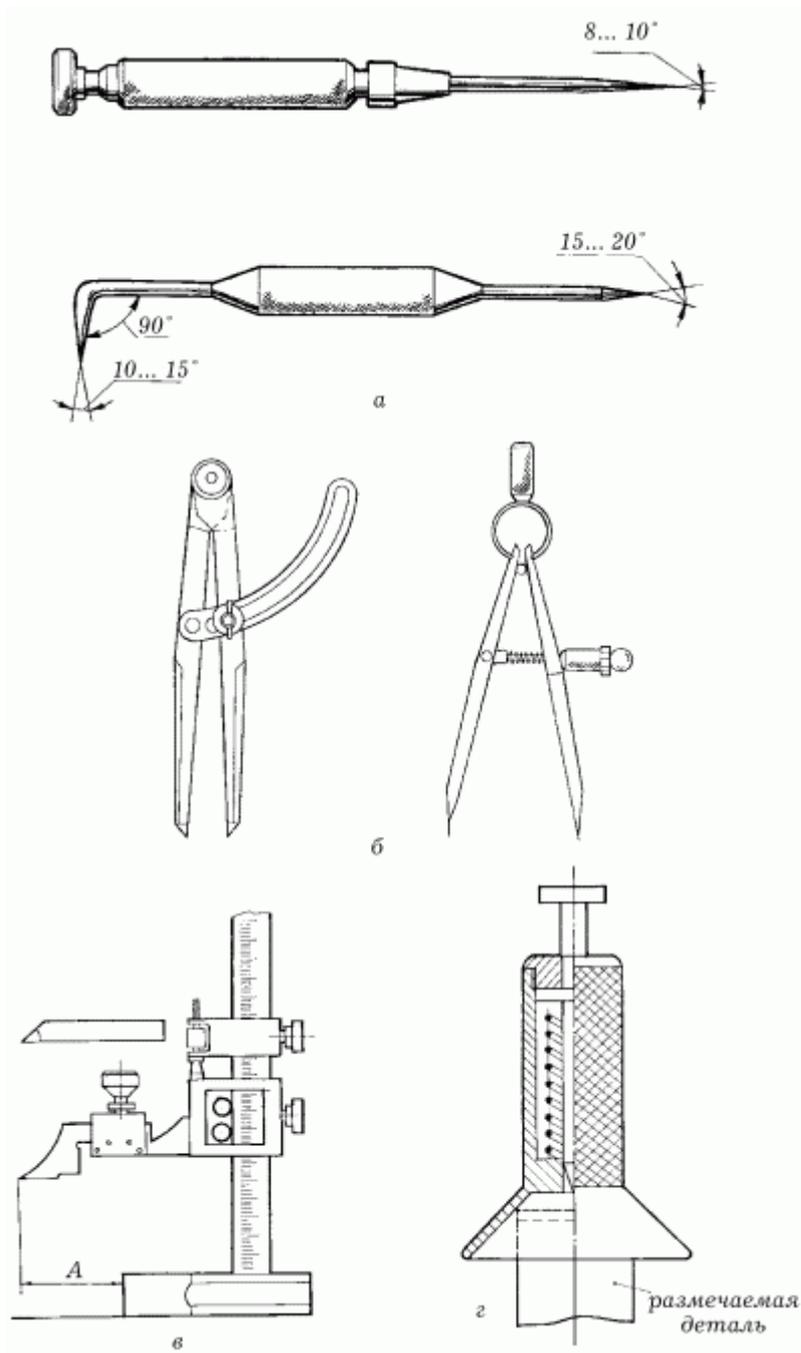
Разметочные инструменты: а – чертилки; б – циркули; в – штангенрейсмус; г – кернер-центроискатель.
